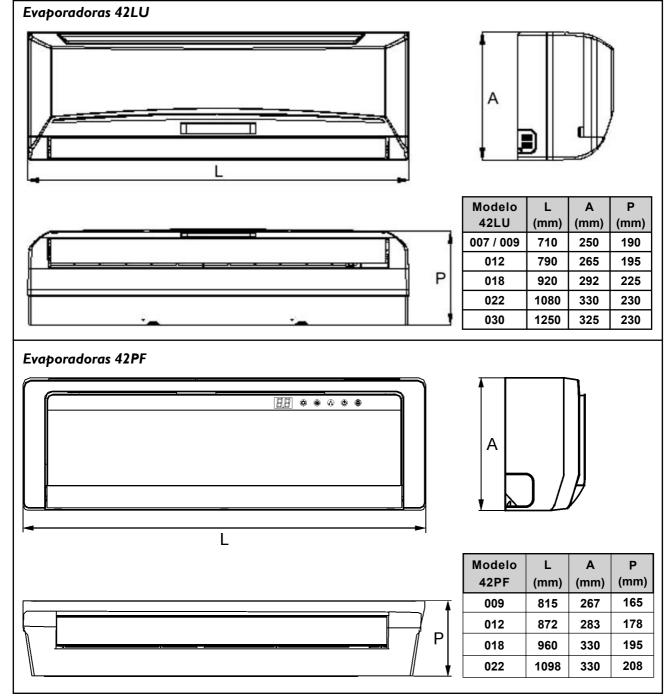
DIMENSIONAL DAS UNIDADES EVAPORADORAS
